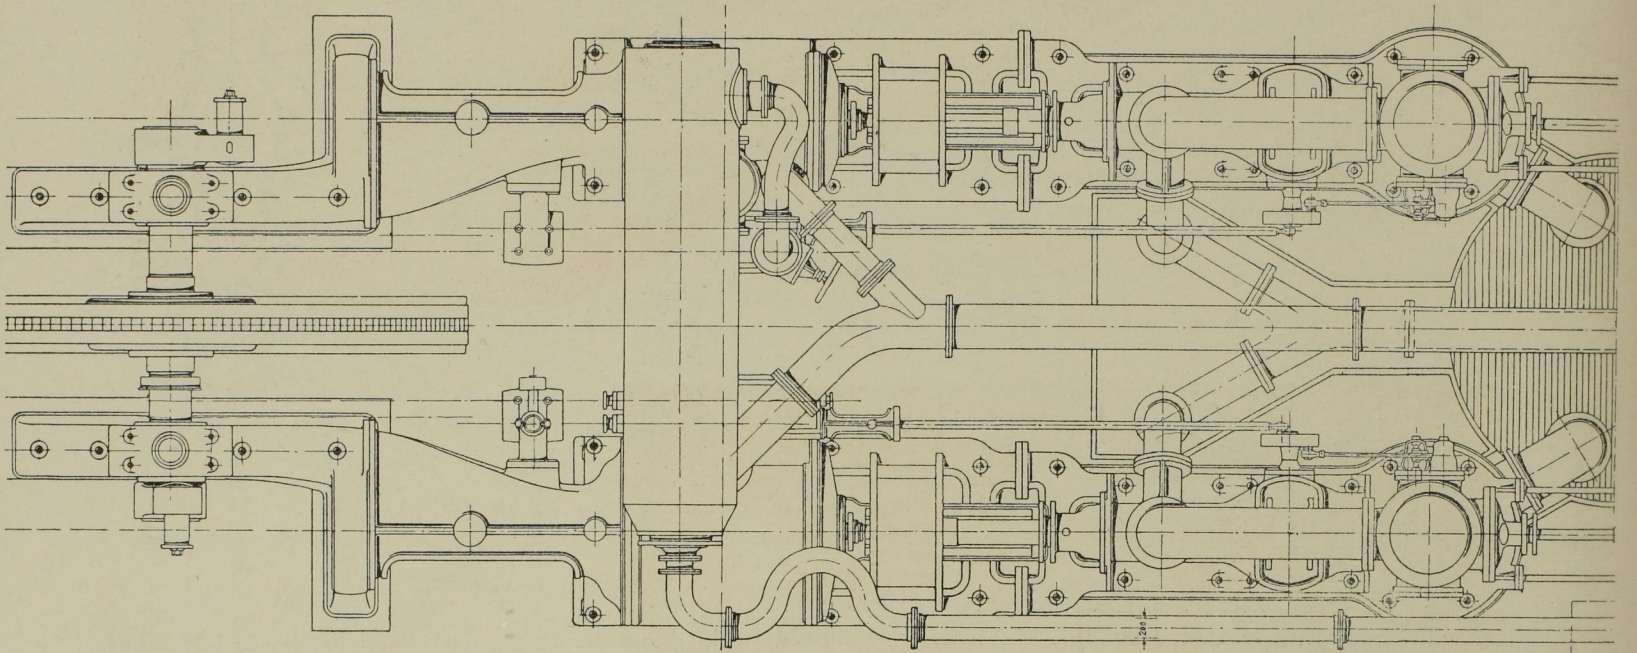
Grundriss der Maschine. Masst. 1:60.
